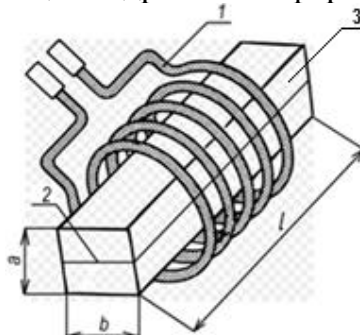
Пространственная модель нагрева клеевого шва с ферромагнитным наполнителем цилиндрическим индуктором:
